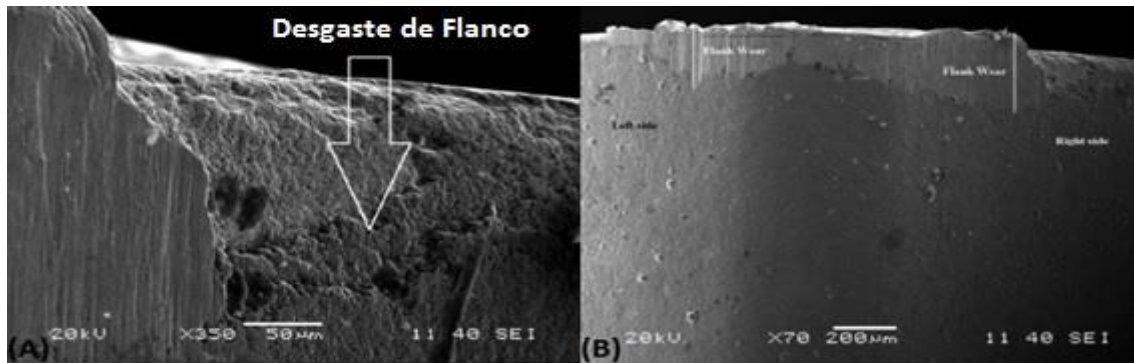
Desgaste de flanco de um inserto de metal duro em usinagem da liga Inconel 718: (A) aumentado 350x; (B) aumentado 70x
